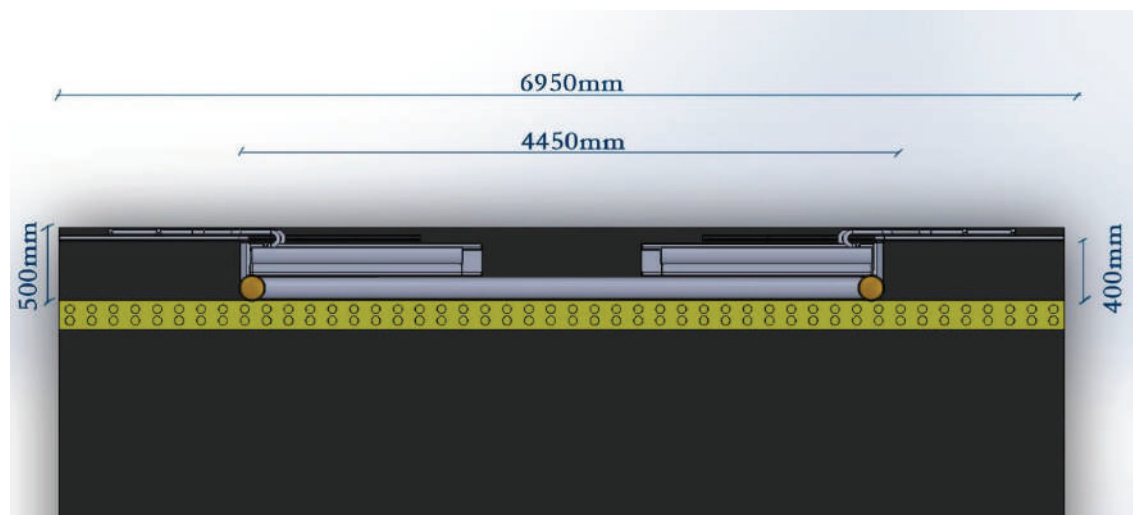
Dimensionamento superior. Fonte: Pelo autor
